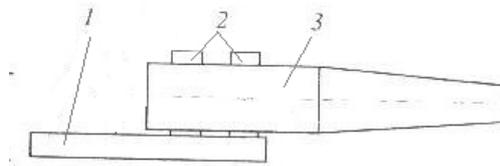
Общий вид сталеалюминиевого анодного штыря.
